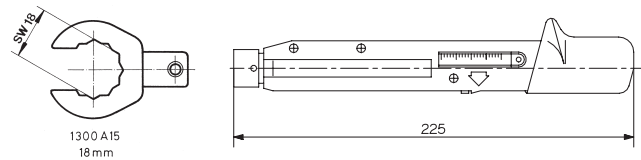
Drehmomentschlüssel 4 ... 20 N·m Typ 1300A39 und Mauleinsätze Typ 1300A15 (18 mm) oder 1300A33 (16 mm)
